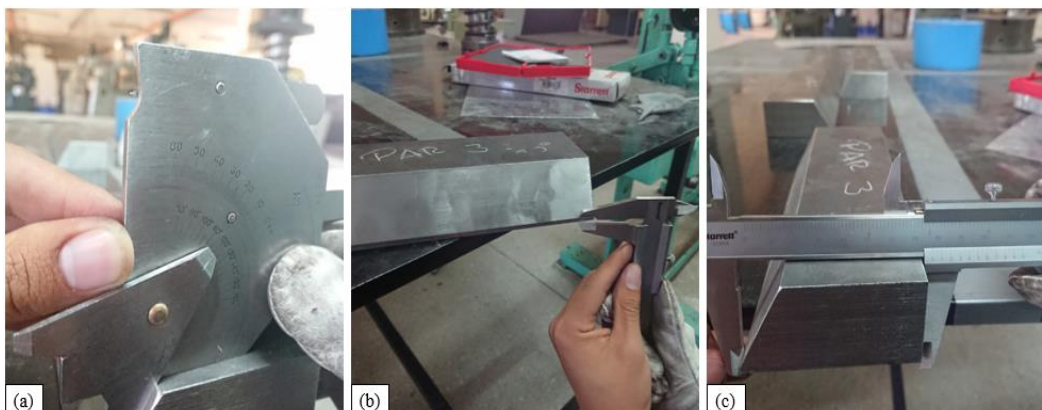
Control de cupones. (a) Control del ángulo del bisel mediante una galga para soldadura. (b) Control de la altura la raíz del cupón. (c) Control del ancho del cupón mediante un calibrador
